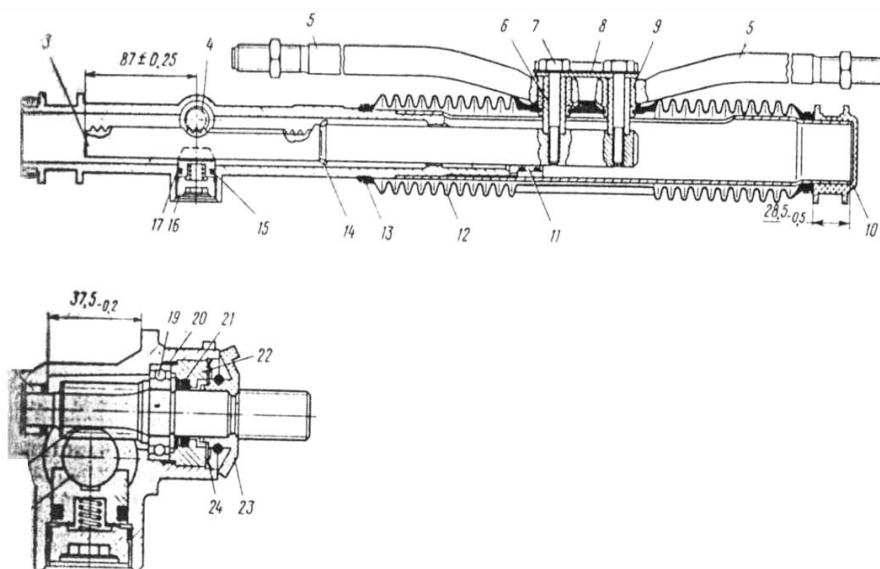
Рульовий механізм рейкового типу з тягою в зборі
